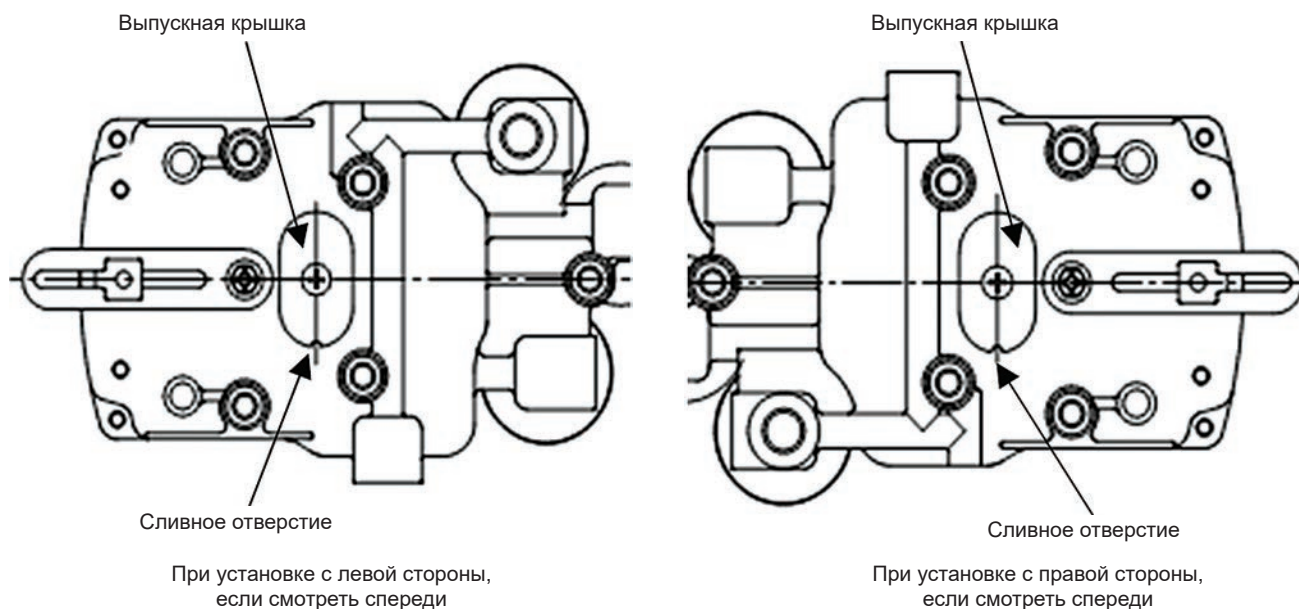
Направление установки позиционера и положение сливного отверстия
